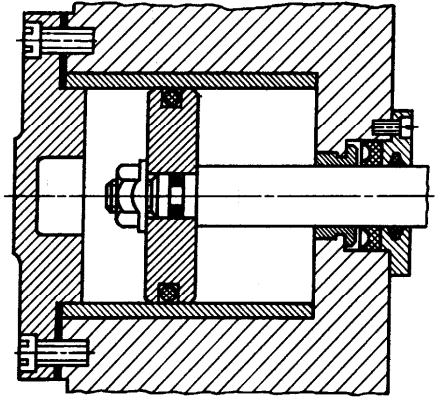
Типовая компоновка встроенного пневмоцилиндра
